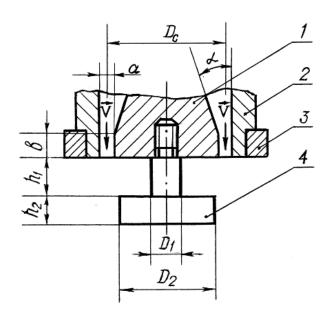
Схема прямоточного ГДИ: 1 — обтекатель, 2 — корпус, 3 — кольцевой насадок, 4 — ступенчатое цилиндрическое препятствие
